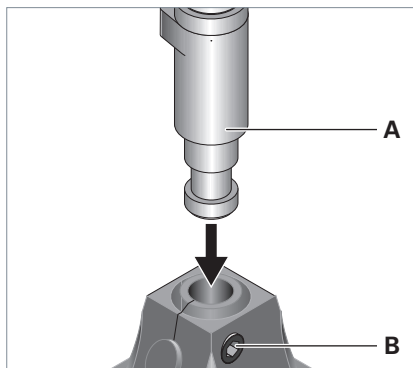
Montare l'apparecchio di illuminazione sull'elemento di fissaggio.
